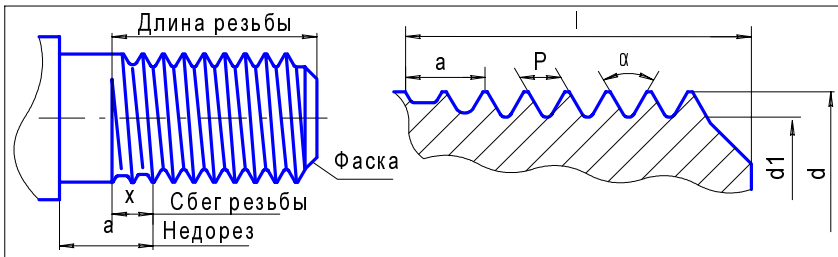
Конструктивные элементы и параметры цилиндрической резьбы
